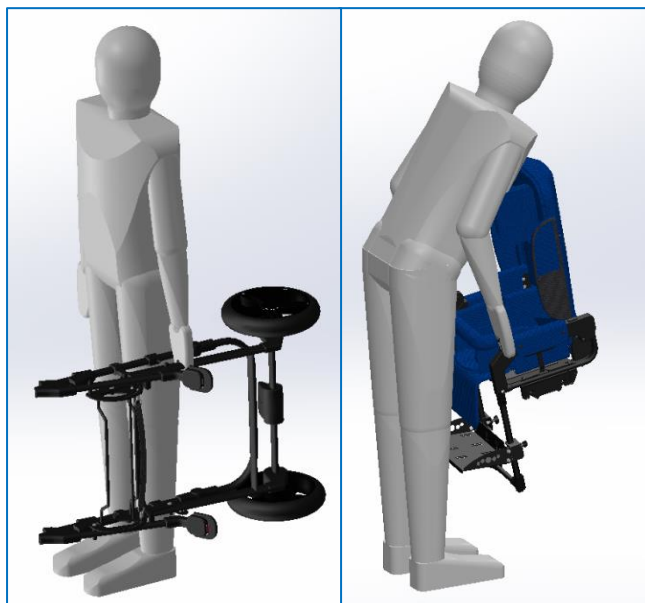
Konstrukcja wózka pozwala na zamocowanie siedziska przodem jak i tyłem do kierunku jazdy
